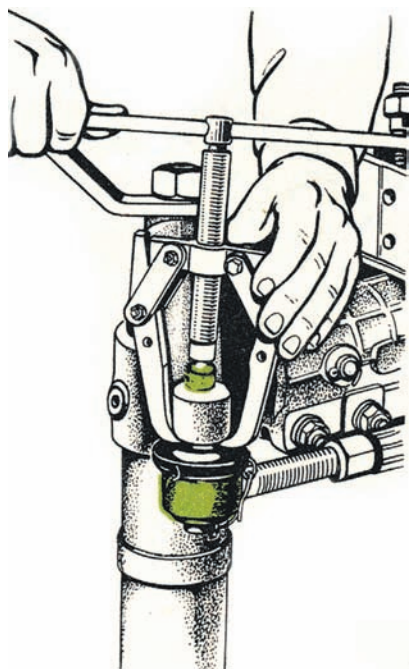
Выпрессовка шарового пальца рулевой тяги из поворотного рычага:
